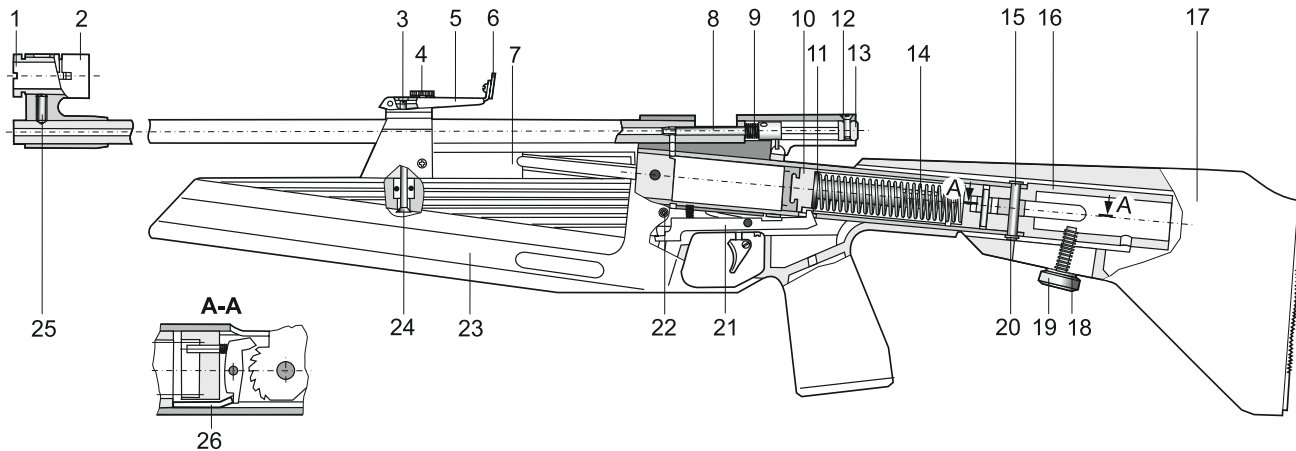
Сборочные единицы и детали винтовки ИЖ-60 – вариант 2
